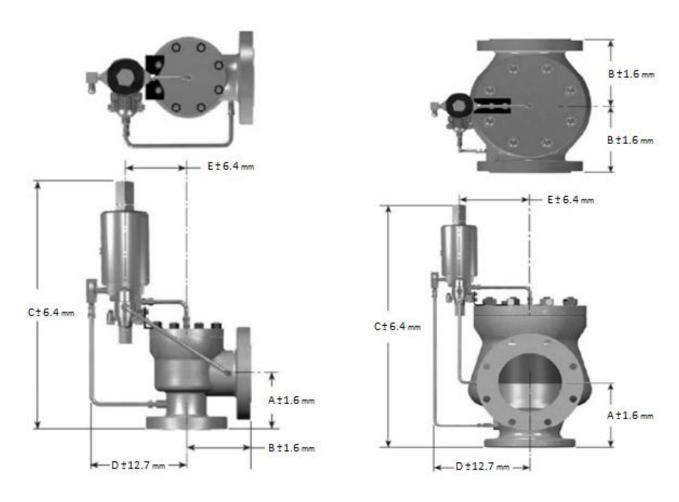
Габаритные размеры полнопроходного клапана предохранительного
